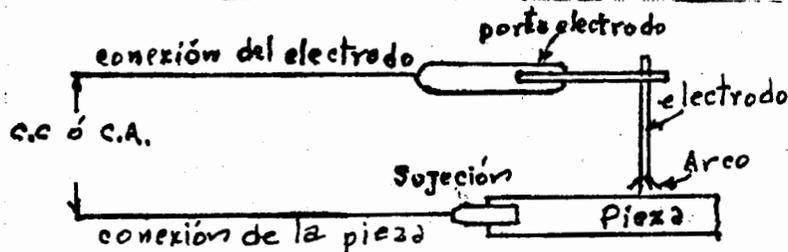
CIRCUITO BASICO DE LA SOLDADURA DE ARCO.
